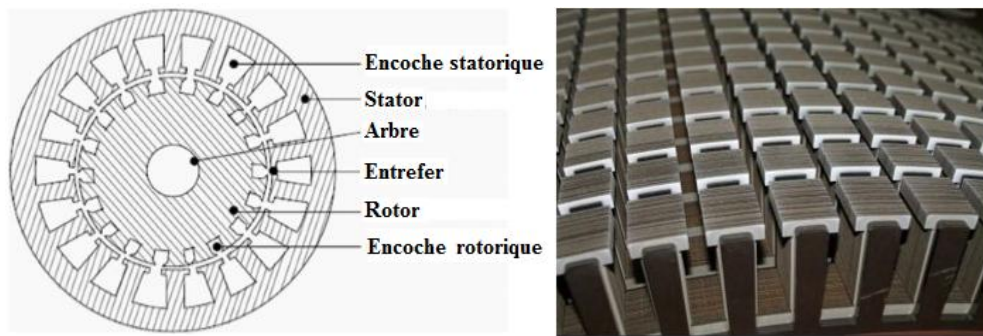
Stator de la machine asynchrone avec le bobinage
